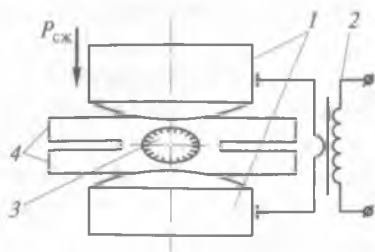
Схема двухсторонней контактной точечной сварки:
